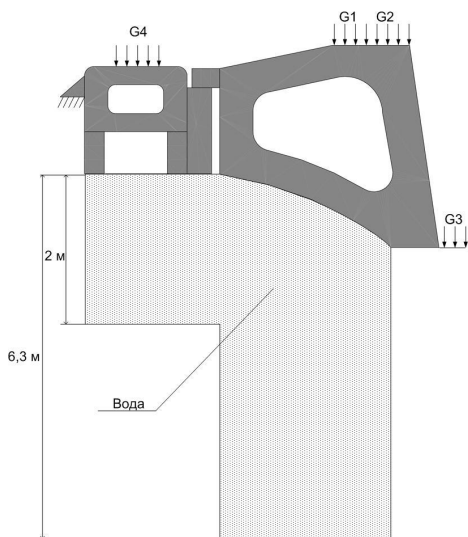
Схема нагружения и закрепления конструкции с верхним кольцом
